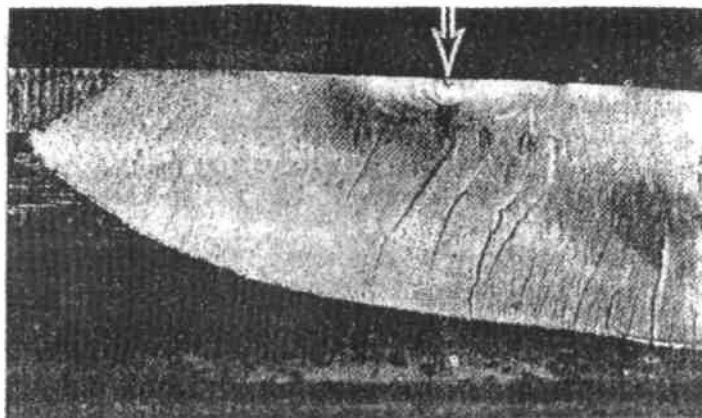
Осередок руйнування на поверхні злому зуба шестерні
